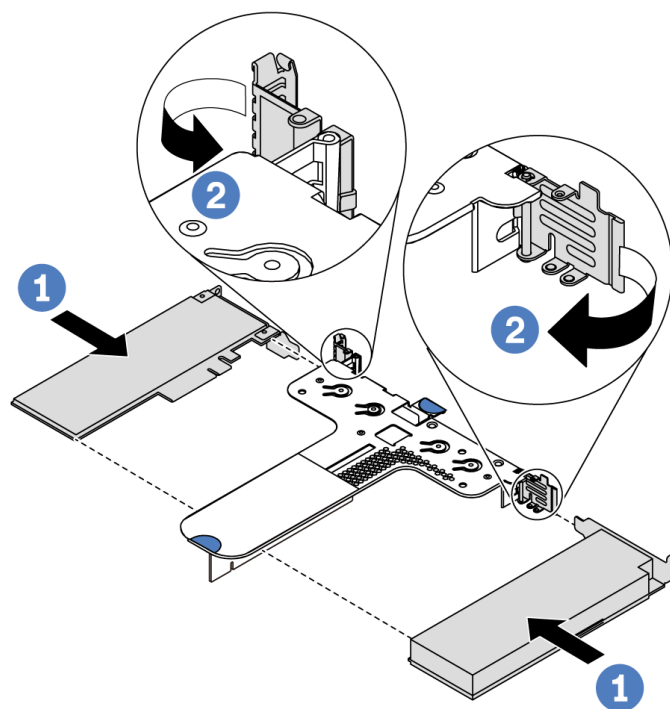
Installazione dell'assieme verticale 2 (LP+LP)
